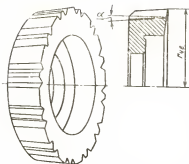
Конструктивные параметры задней поверхности долбяков, когда эта поверхность является цилиндрической
